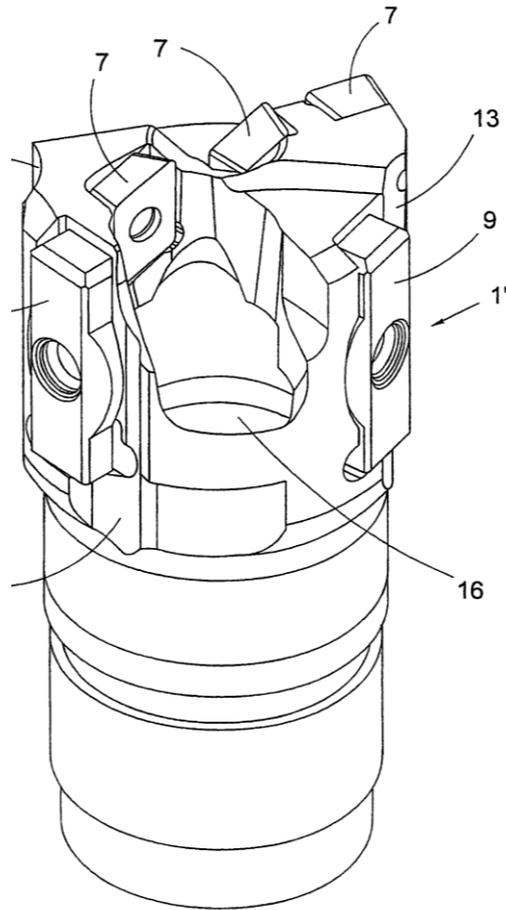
Обнижения для СОЖ на торце корпуса головки
